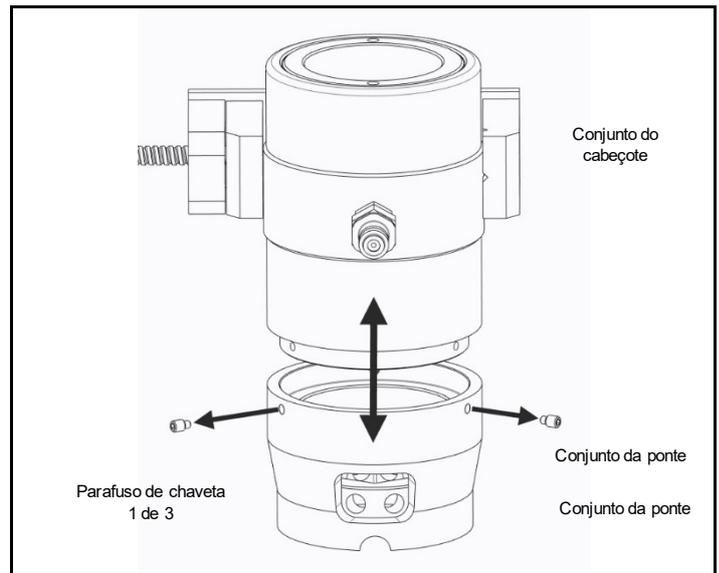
Separação do conjunto do cabeçote e do conjunto da ponte
